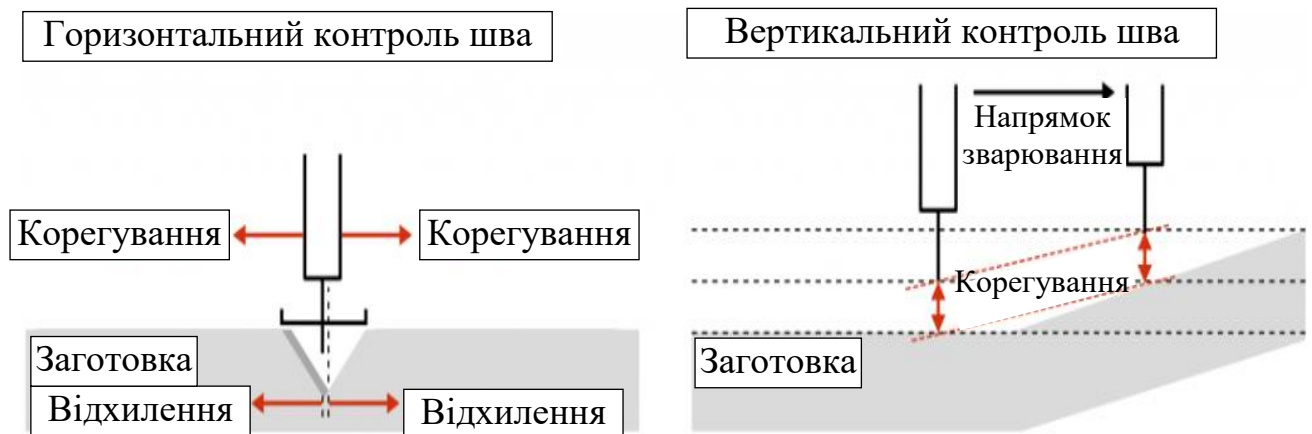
Функція стеження за параметрами шва під час зварювання зчепи автозчепного пристрою
